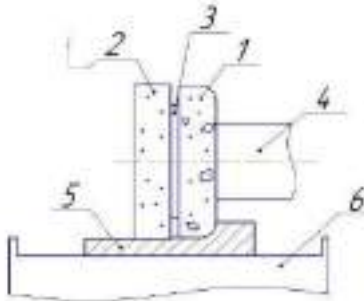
Обработка заготовки одновременно двумя шлифовальными кругами
